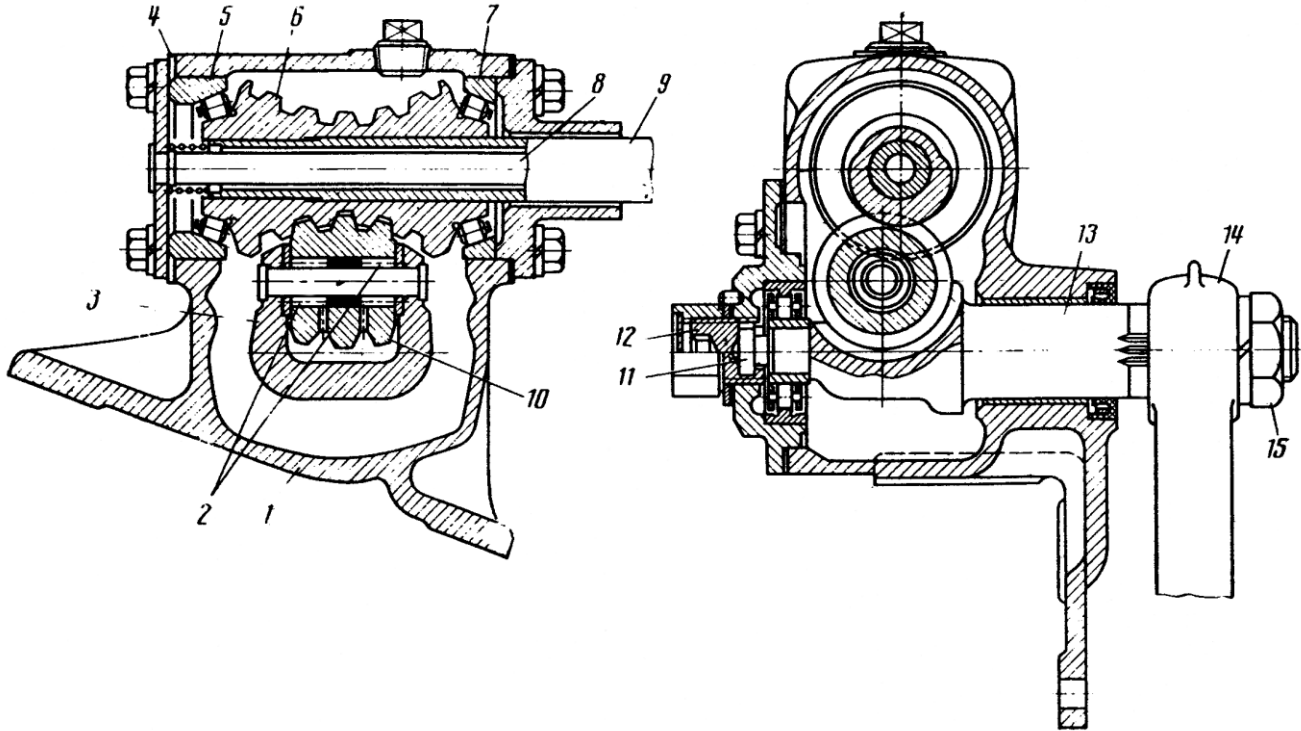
Рулевой механизм автомобиля ГАЗ-53А:
